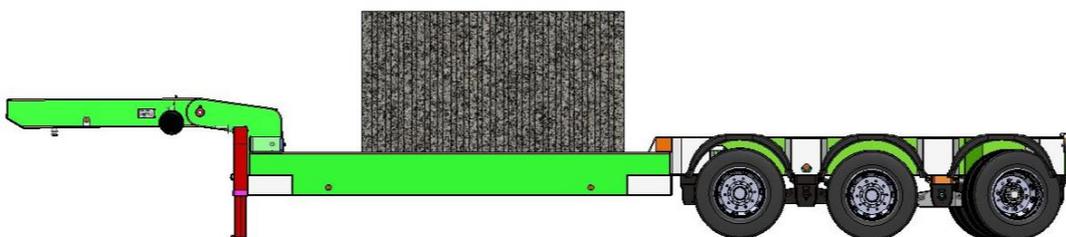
Vista lateral do equipamento proposto carregado em formato 3D. Fonte: Próprio Autor (2018)
